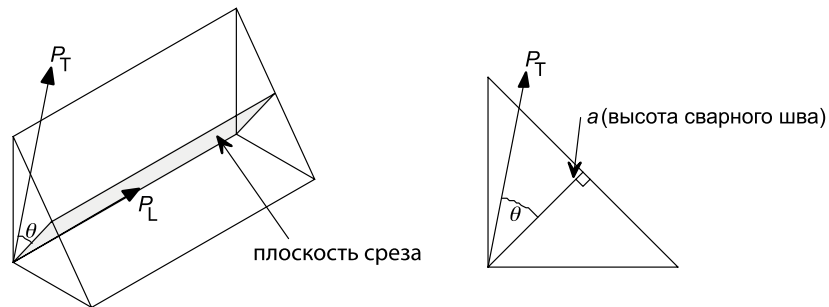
Обозначения к расчету сварных швов
